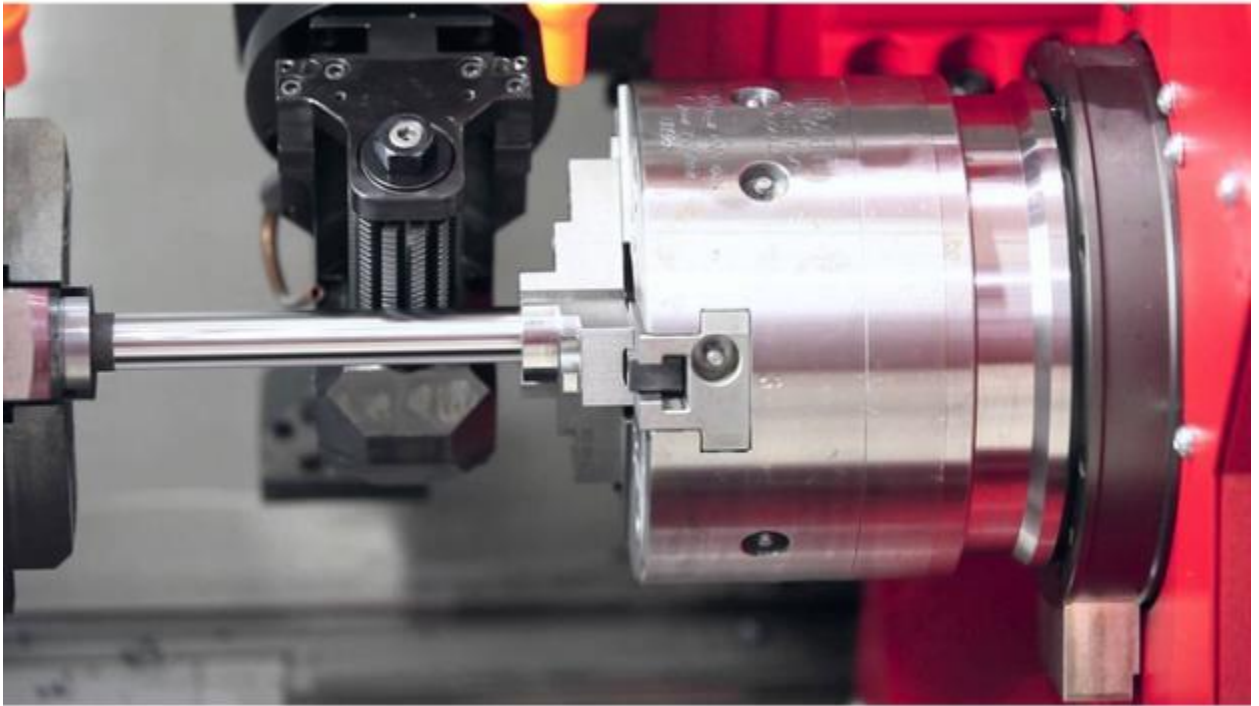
Два шпинделя верстату MAXXTURN 65
